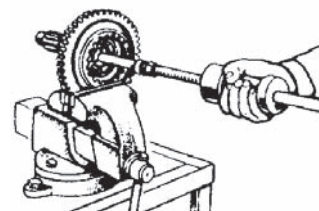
Выпрессовка подшипника № 208 из вторичного вала.
